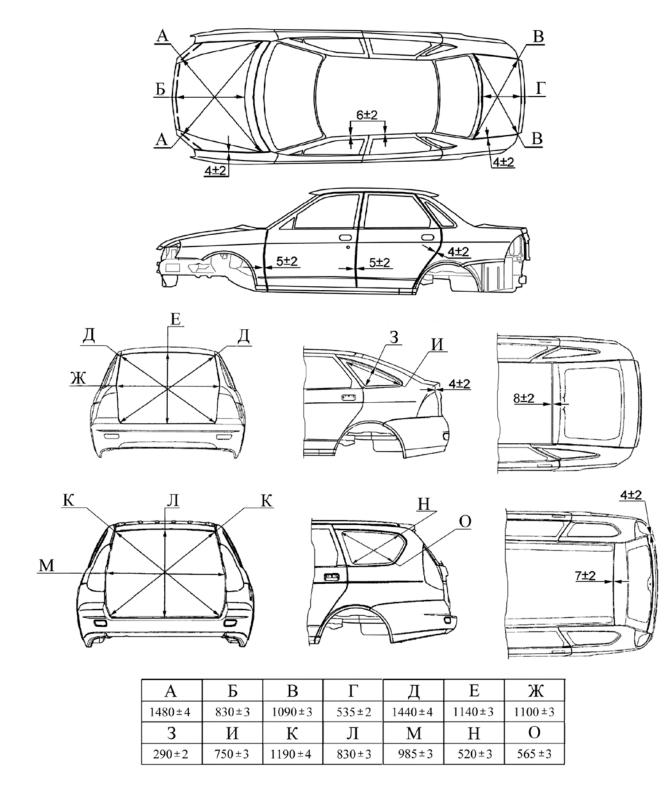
Размеры проемов и зазоры сопрягаемых деталей кузовов 1117, 1119
